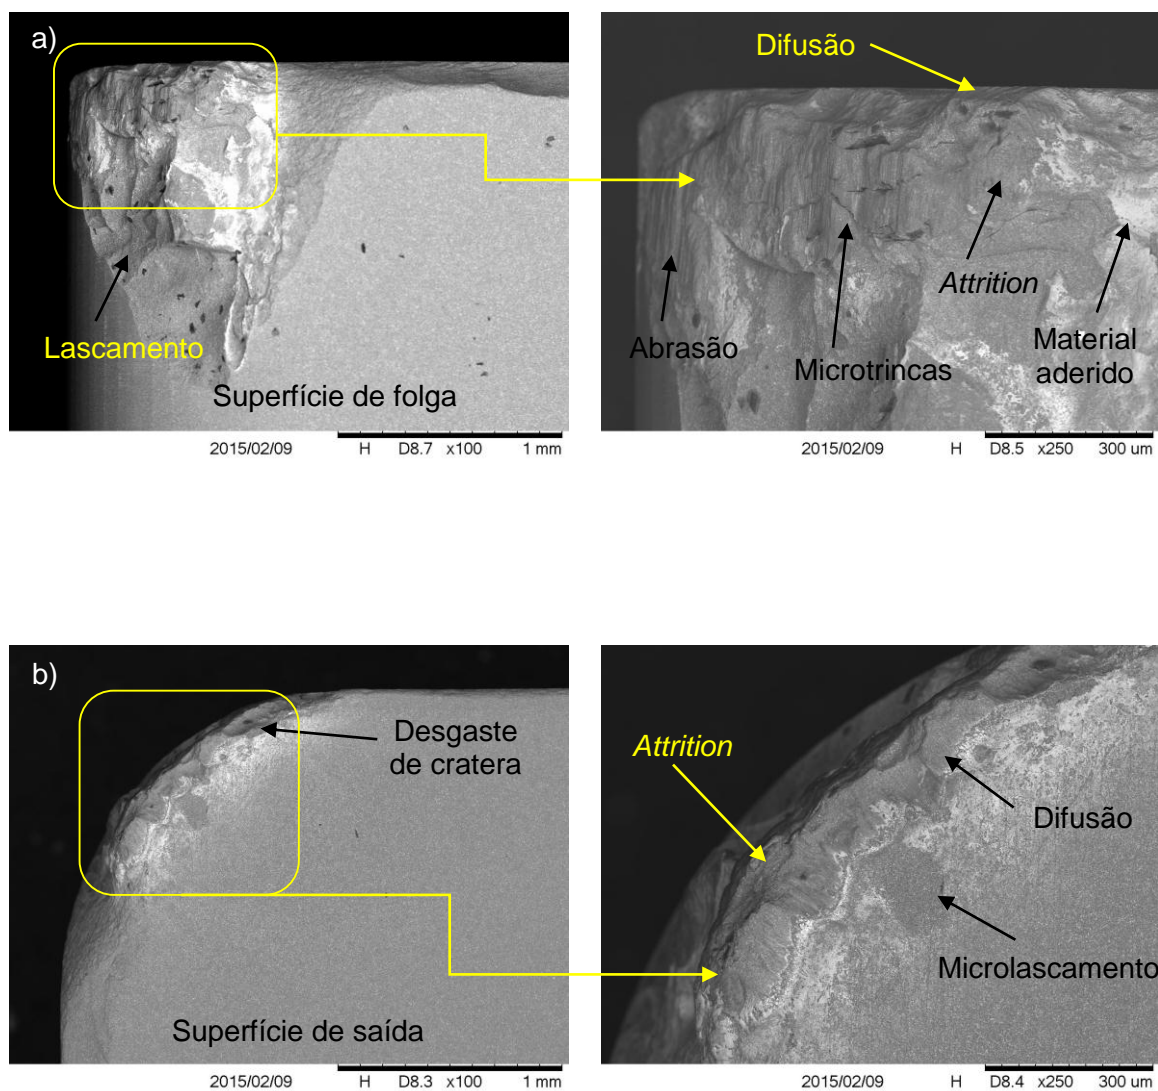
Fotografias obtidas através do MEV das ferramentas mista após a usinagem do Inconel 718 com aplicação de fluido de corte LB 2000 + 20% grafite por MQF. (a) superfície de folga e (b) superfície de saída
